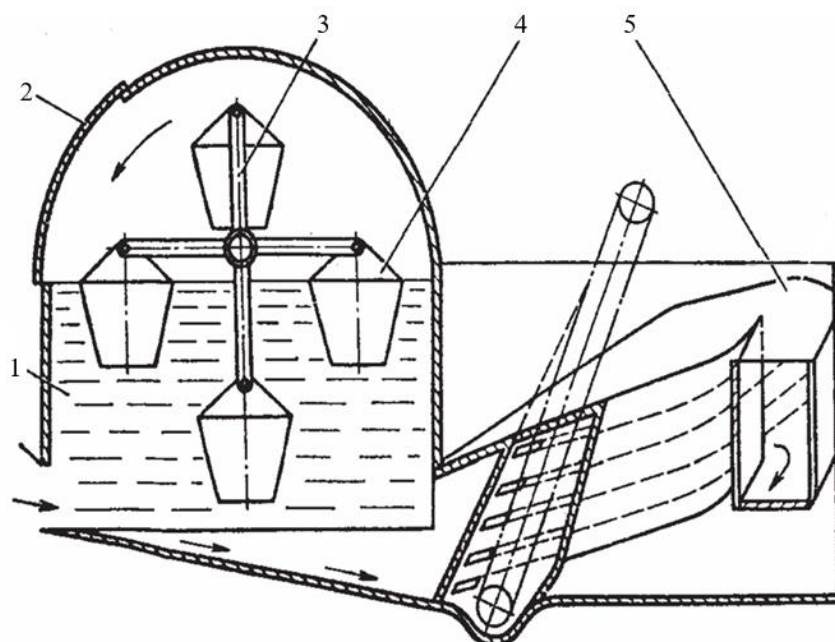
Принципиальная схема установки для очистки деталей погружением: 1 – ванна; 2 – крышка проема для загрузки и выгрузки деталей; 3 – крестовина; 4 – контейнер для деталей; 5 – устройство для очистки растворов от твердых загрязнений
